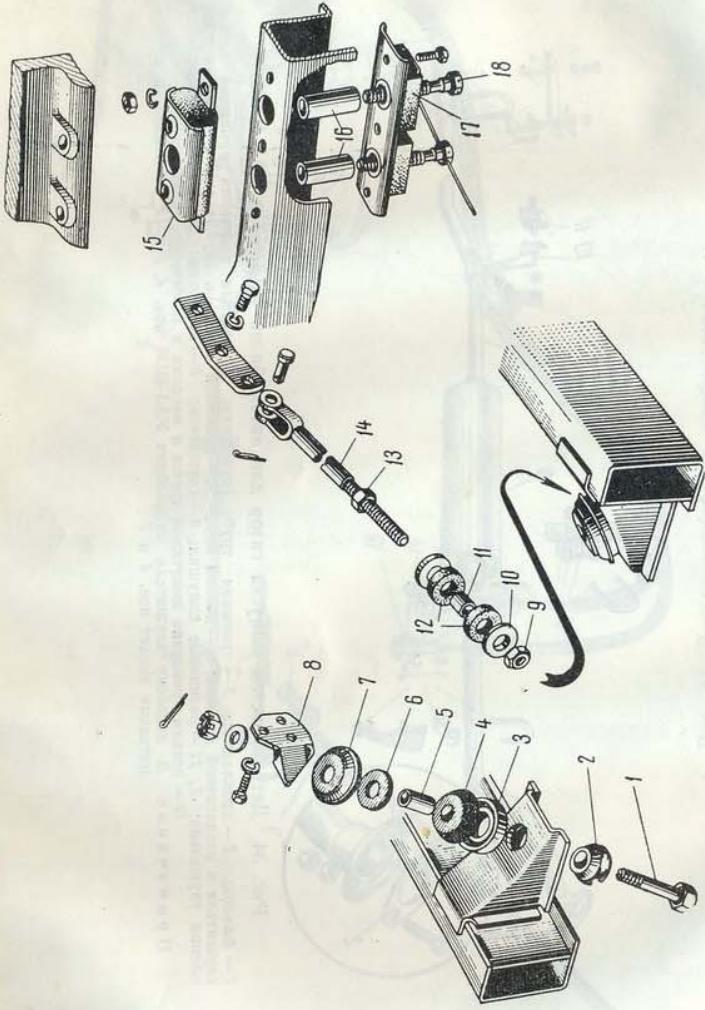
Детали подвески двигателя автомобиля УАЗ-451М:
